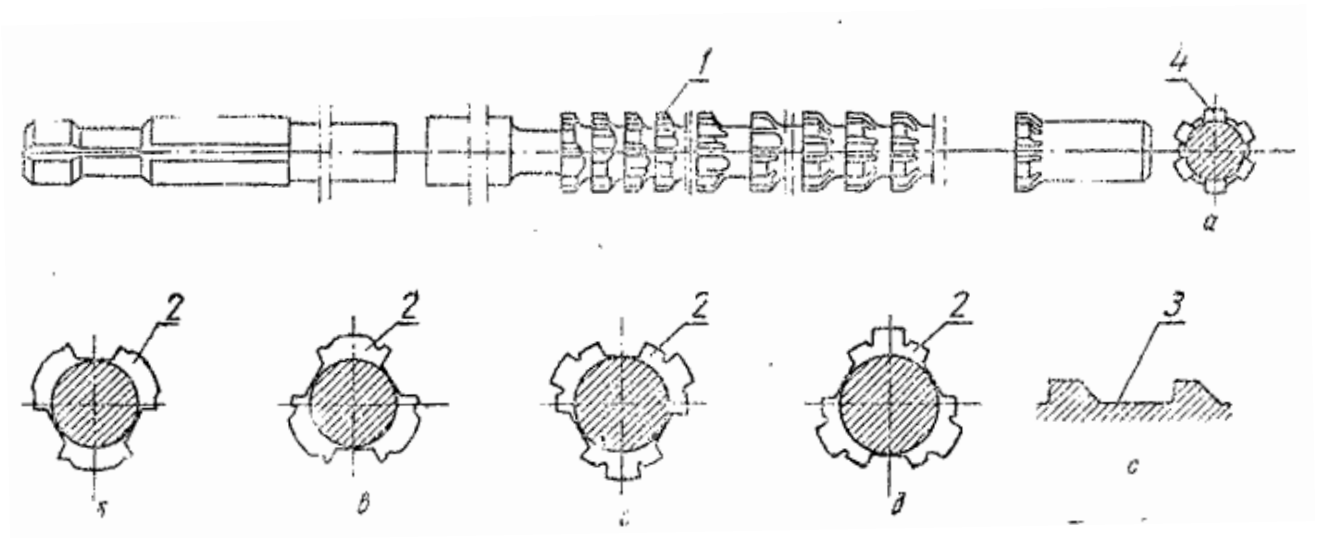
Шліцьова протяжка прогресивного різання [4].
